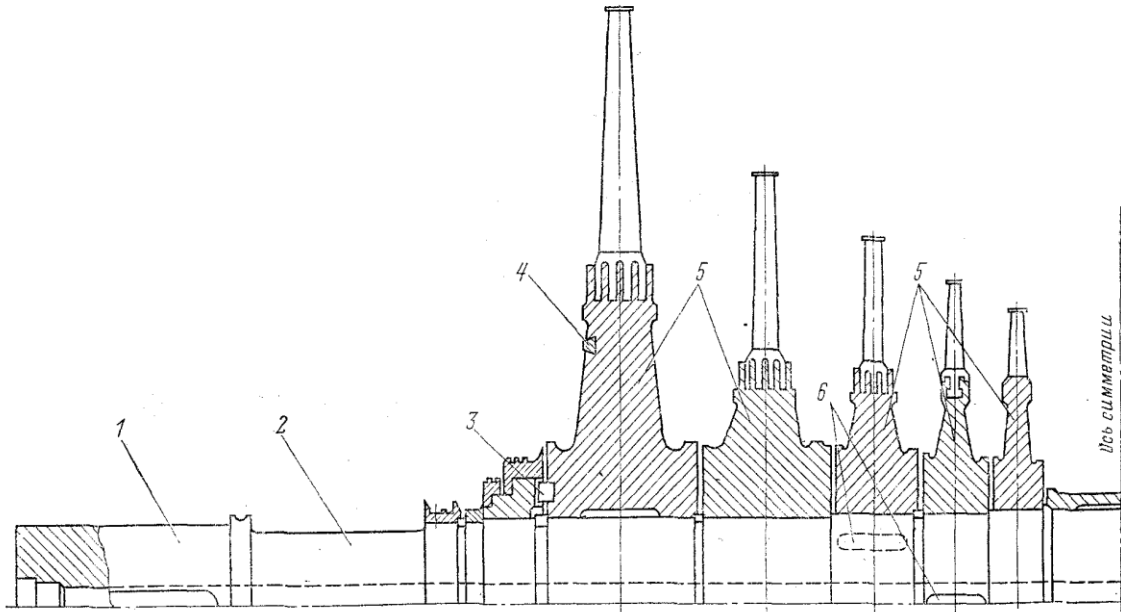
Збірний ротор двопоточного ЦНТ:
